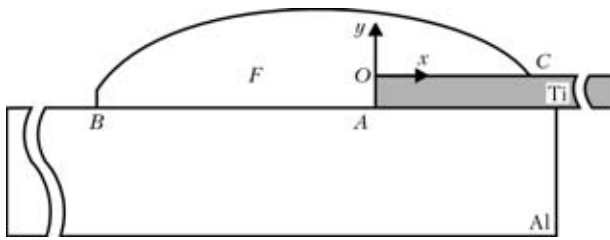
Схема нахлесточного сварного соединения типа титан-алюминий [1, 5]
